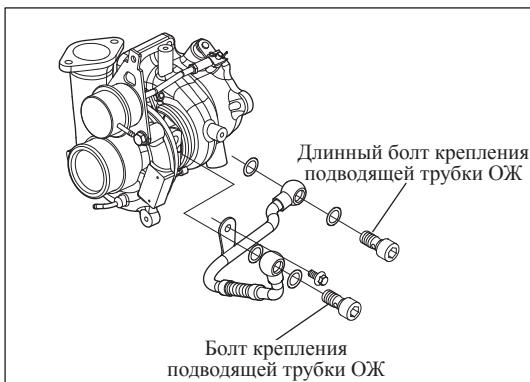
Установка подводящей трубы ОЖ турбонагнетателя
